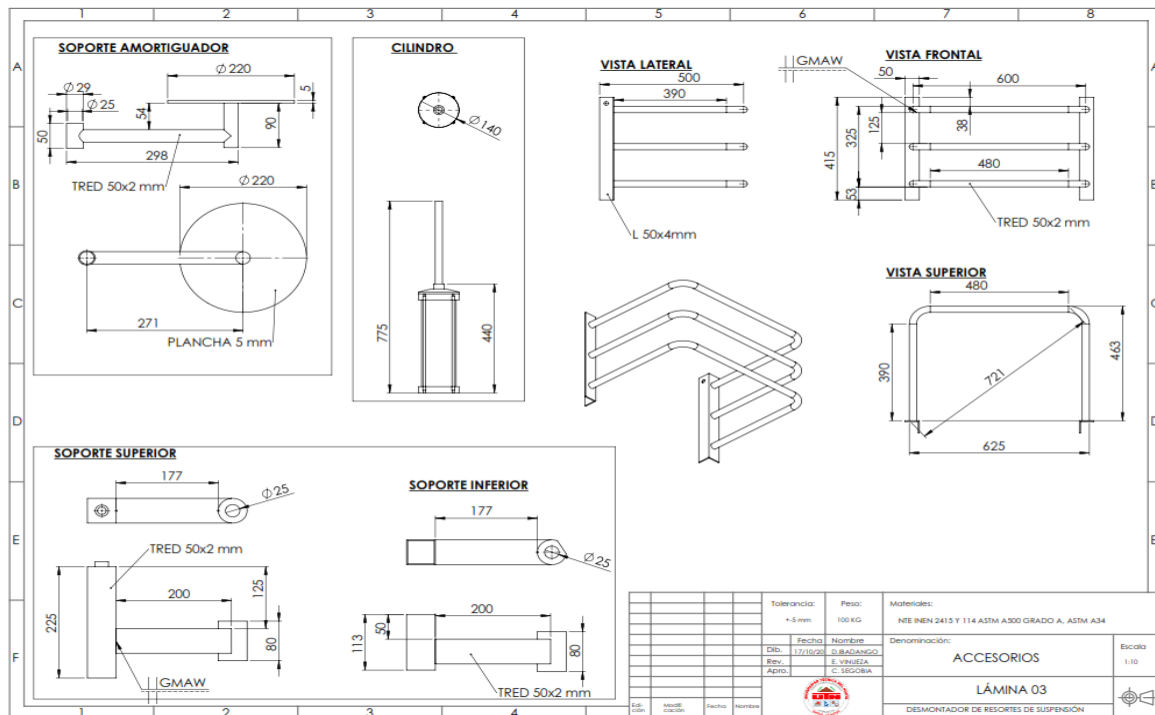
Plano soporte amortiguador y rejilla de protección
